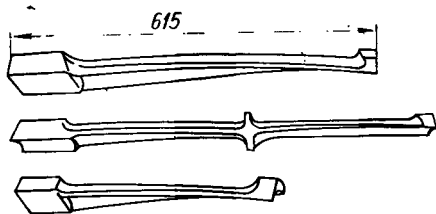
Формы штампованных заготовок для рабочих лопаток
